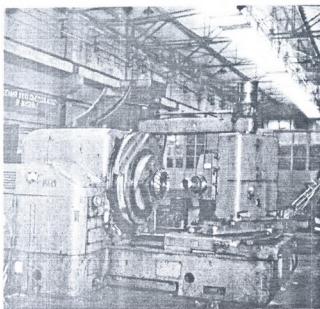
Модернизированный зуборезный станок мод. ZFTKK-500×10 для нарезания некруглых конических колес с круговыми зубьями
